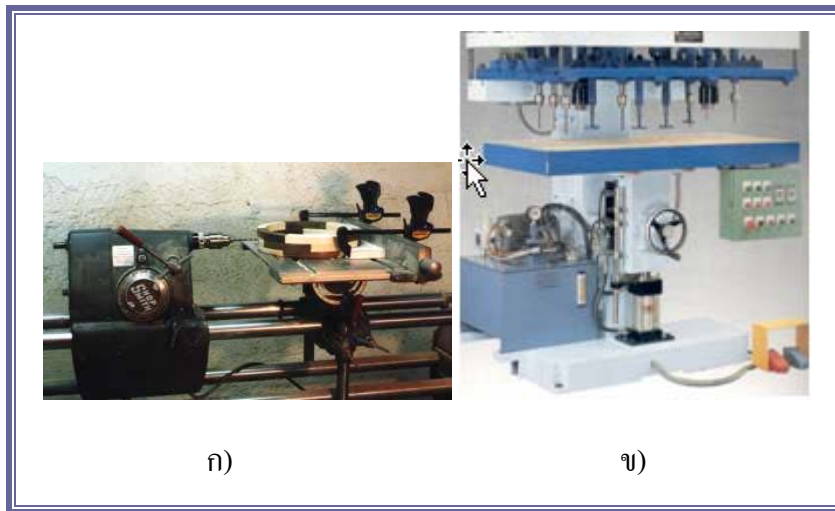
เครื่องหมุนขึ้นรูป (Spindle Molder Machine) เครื่องกลึงไม้ (Turning Lathe) เครื่องเลื่อยสายพาน (Band Saw) และเครื่องลอกแบบอัตโนมัติ (Automatic Copy Shaper)
